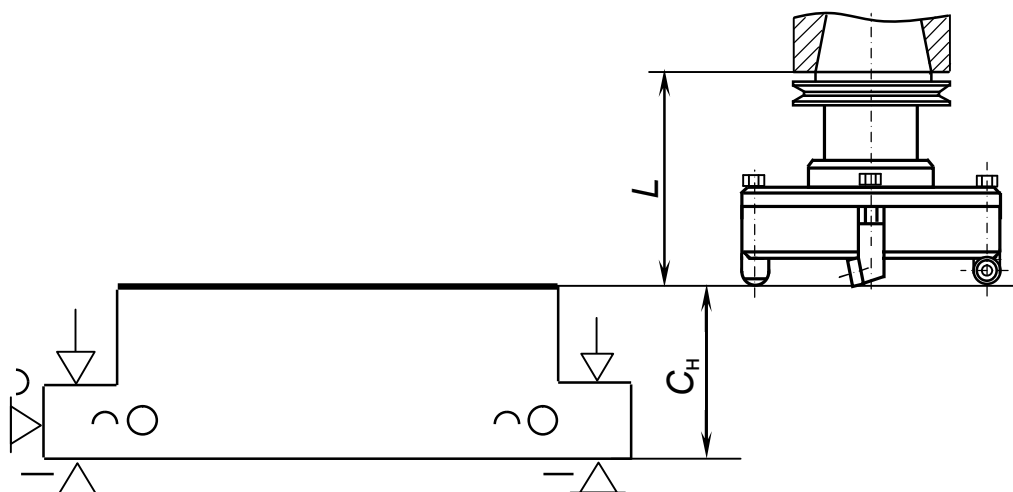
Схема, що пояснює процес настроювання торцевої фрези на розмір обробки
